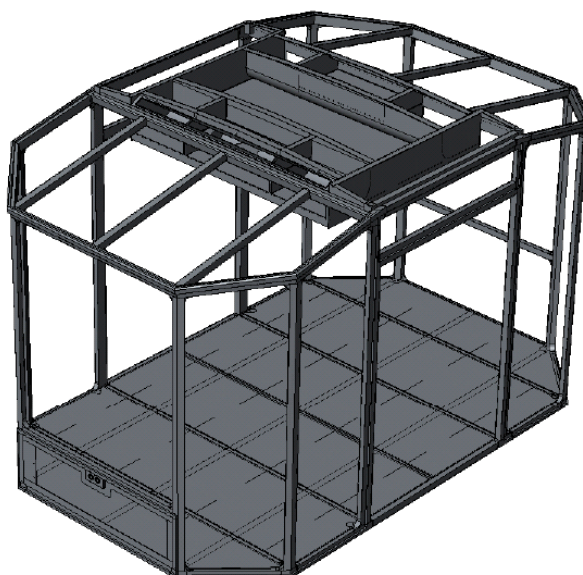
Сварной каркас кузова транспортного модуля
